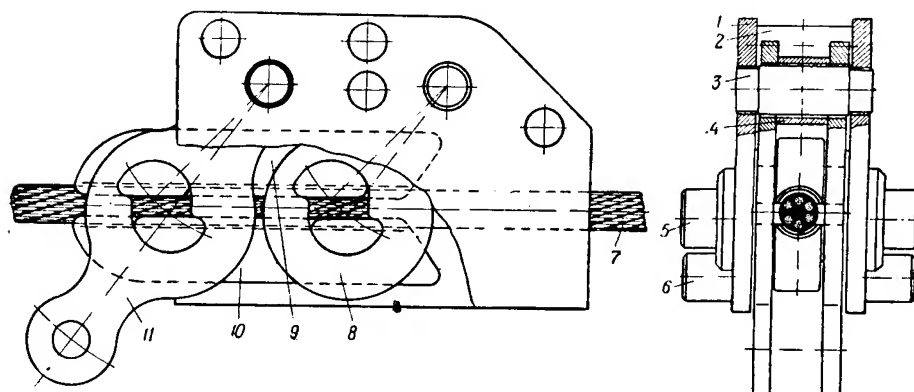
Самозажимной захват: 1 — щека; 2 — стойка; 3 — ось; 4 — распорная втулка; 5 — ось рычага; 6 — упор; 7 — трос; 8 — малое коромысло; 9 — верхний зажим; 10 — нижний зажим; 11 — большое коромысло.
